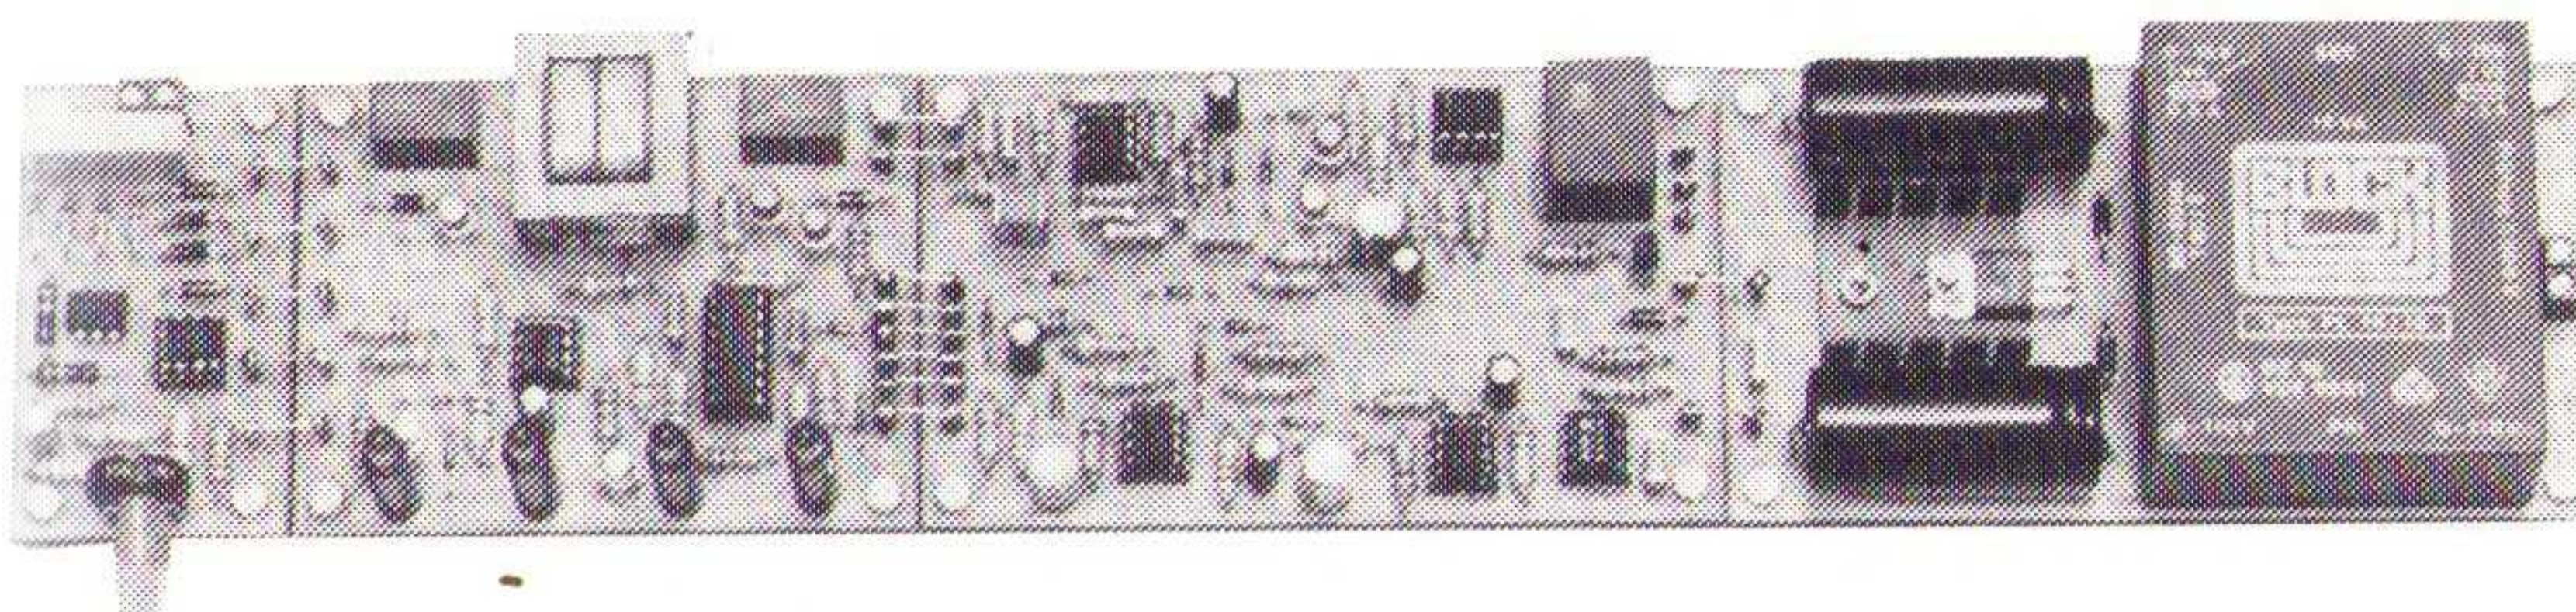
De compleet gemonteerde besturingsautomaat.
